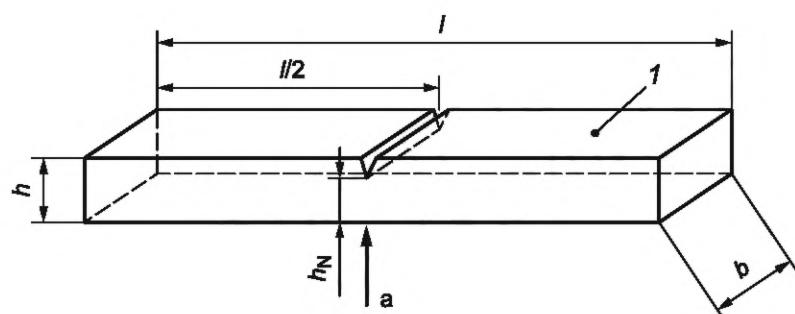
Расположение для образцов типов 6, 7, 8 и 9
